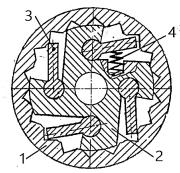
Поворотный механизм с четырьмя собачками в корпусе: 1 — храповое кольцо; 2 — храповой стержень; 3 — собачка; 4 — пружина.
